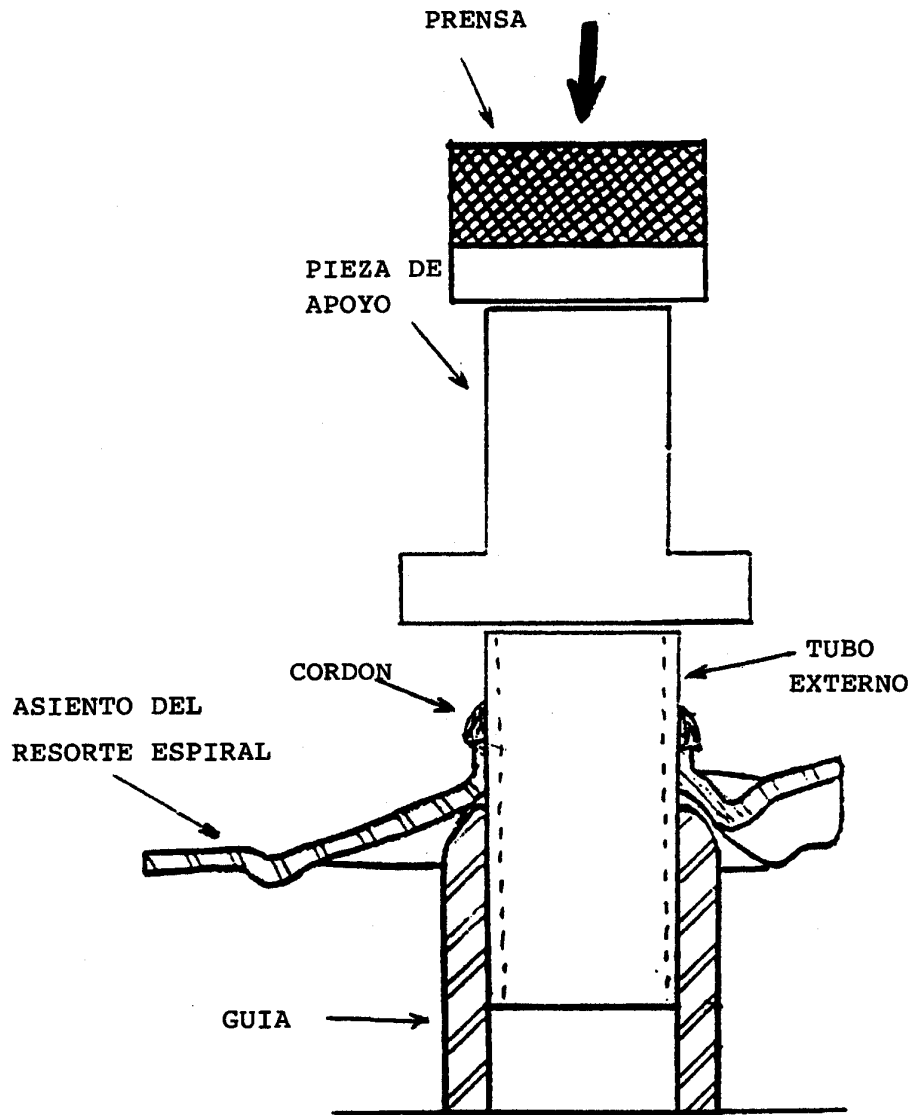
Esquema típico del dispositivo de ensayo para resistencia estática de la soldadura.
